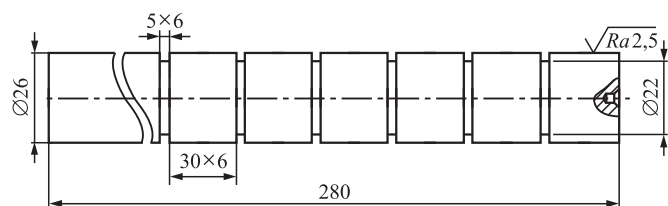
Экспериментальный образец для оценки шероховатости упрочненных поверхностей
